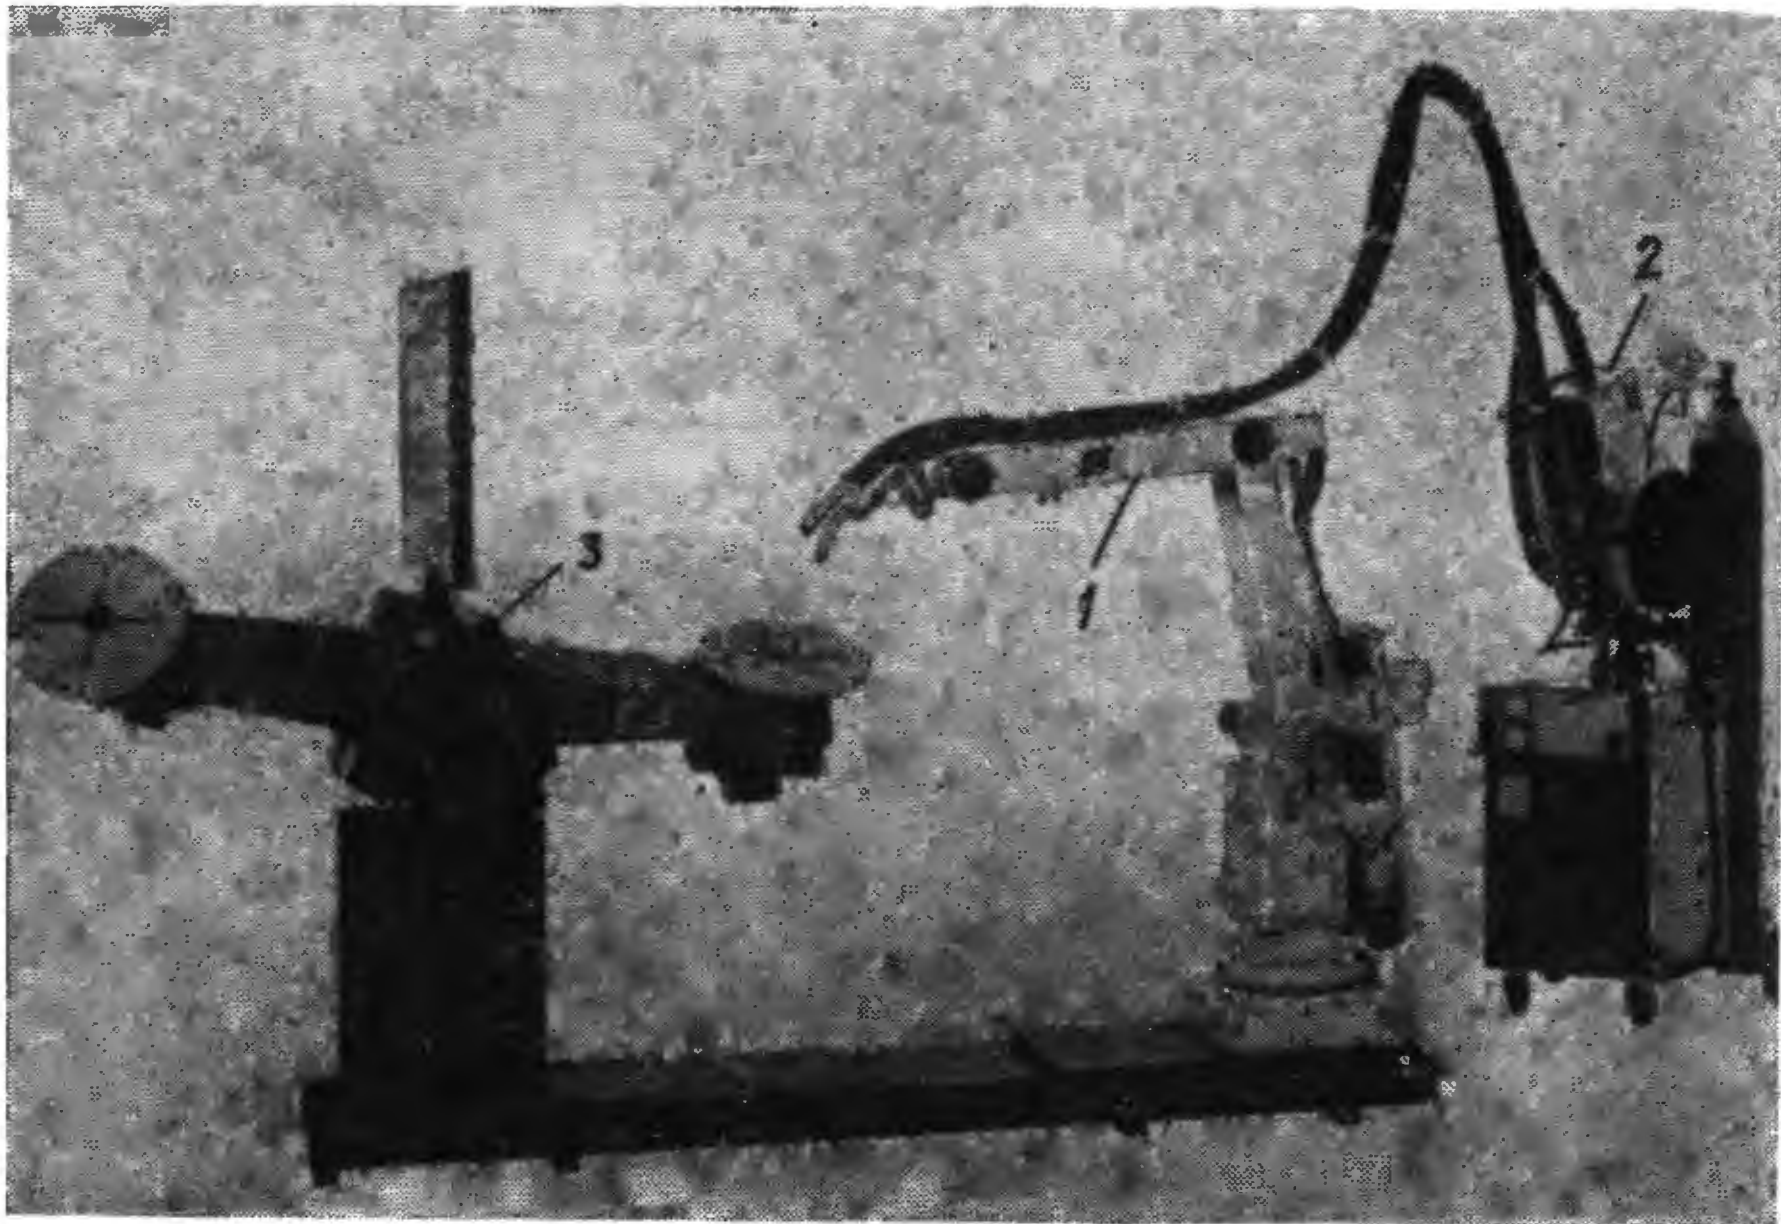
Робототехнический комплекс фирмы ЭСАБ (Швеция) для дуговой сварки с двухпозиционным столом:
